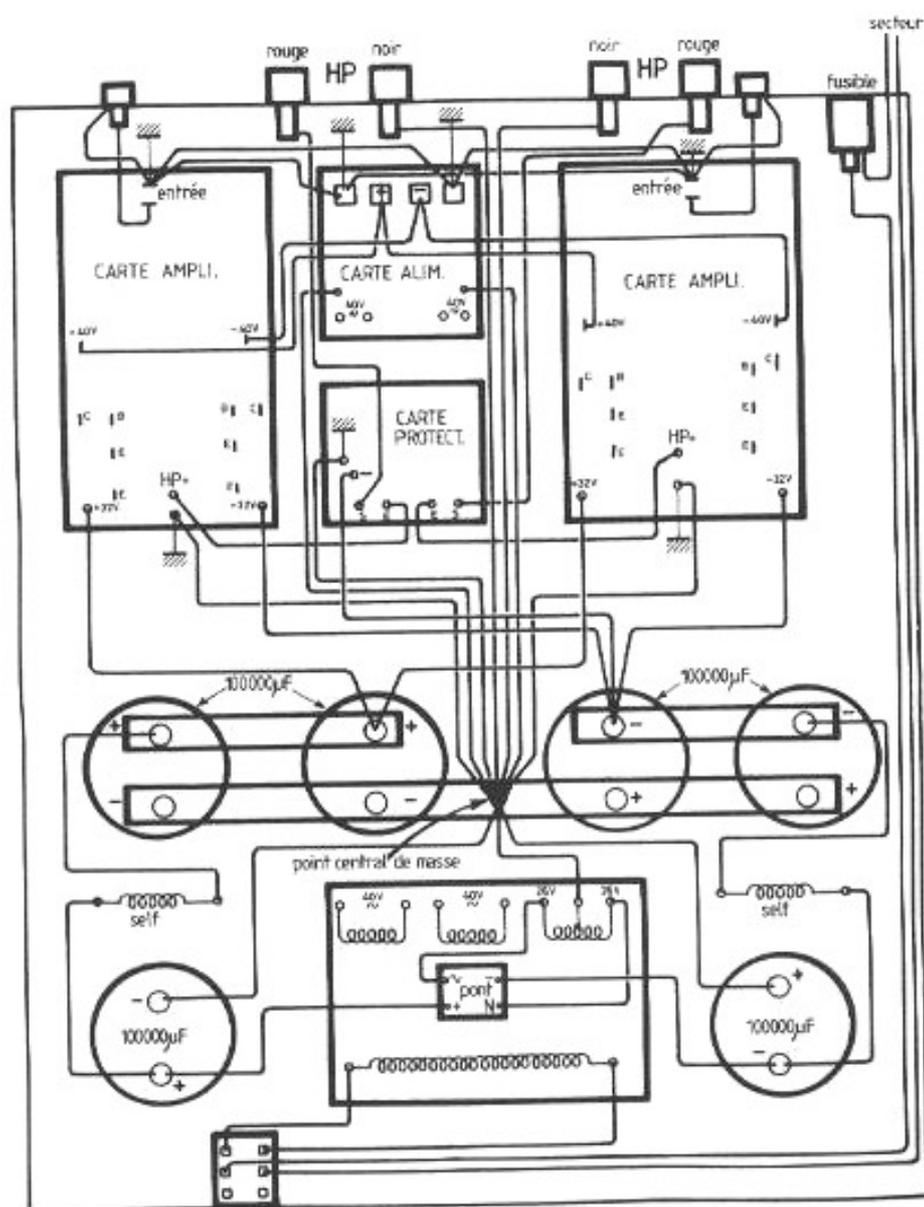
Plan de câblage. On notera le point de masse central illustré sur les photos ci-contre.
